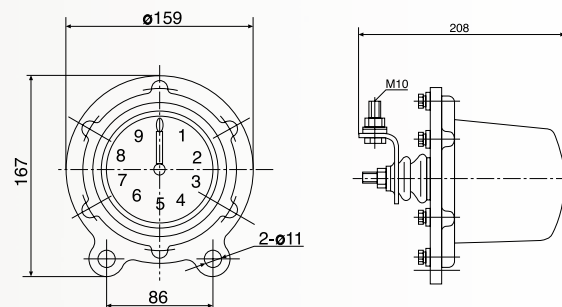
JS-9 放电计数器外形、接线端子及安装尺寸
